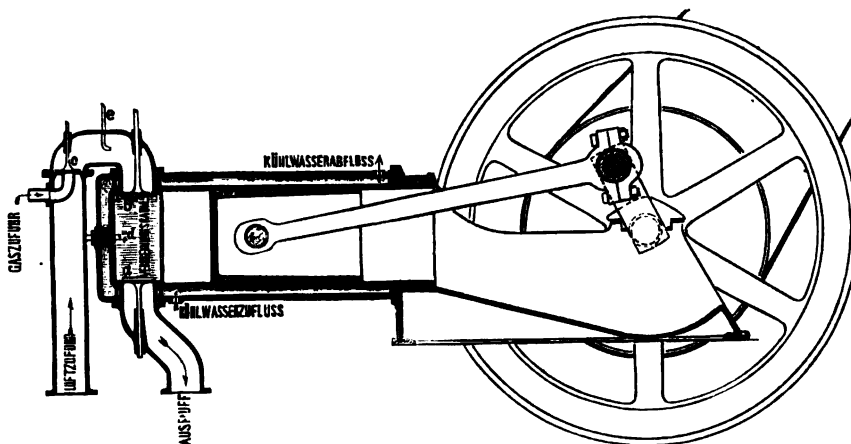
Schematischer Längsschnitt einer Gasmaschine.
